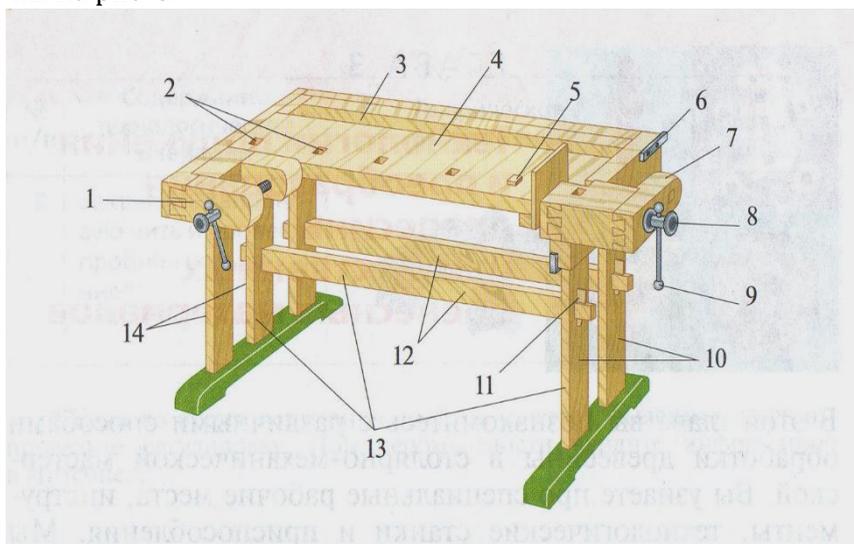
Основные части столярного верстака: 1- передний зажим с закруткой и головкой винта; 2 - гнезда; 3 - лоток; 4 - столешница; 5 - клин; 6 - упор; 7 - задний зажим; 8 - головка винта; 9 - закрутка; 10 - задние ножки; 11 - клин подверстачья; 12 - связи; 13 - подверстачье; 14 - передние ножки
